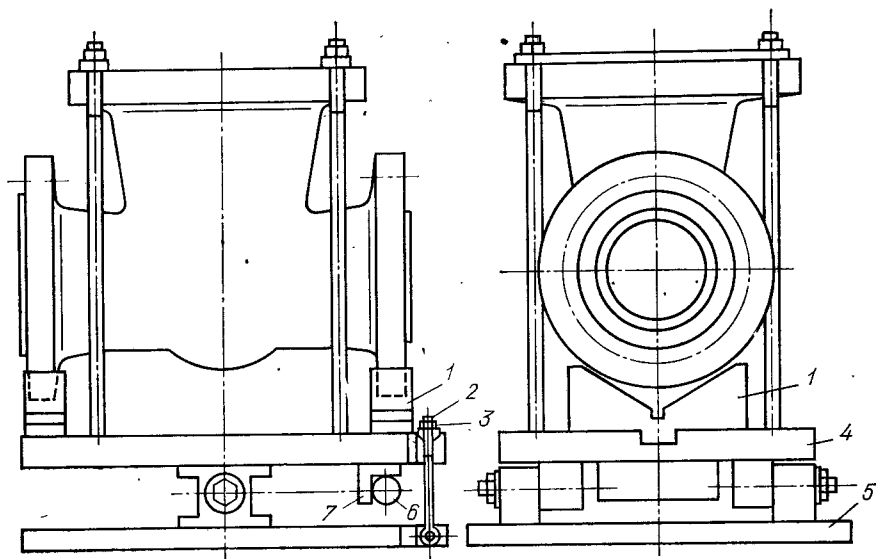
Приспособление для обработки уплотнительных колец корпуса клиновидной задвижки:
